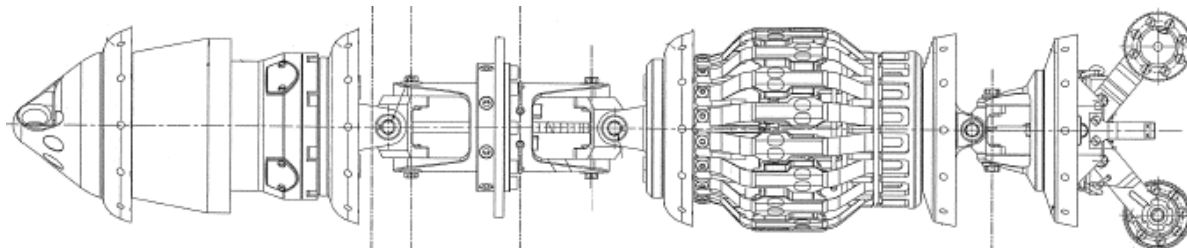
Чертеж общего вида дефектоскопа внутритрубного магнитного 6-МСК.01-00.000-01
